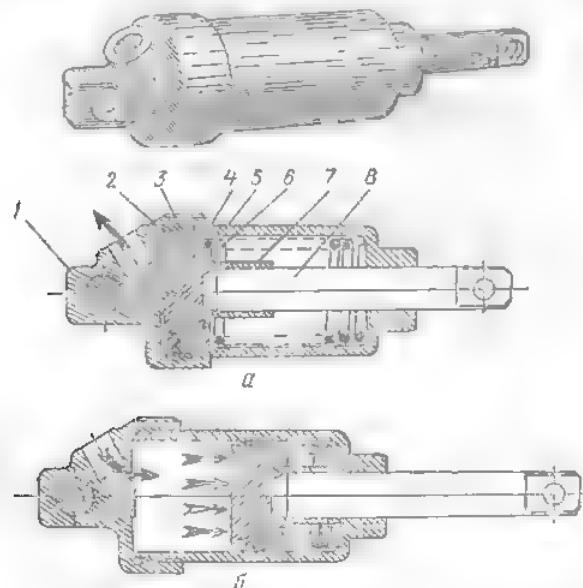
Пневматический цилиндр прекращения подачи топлива:
